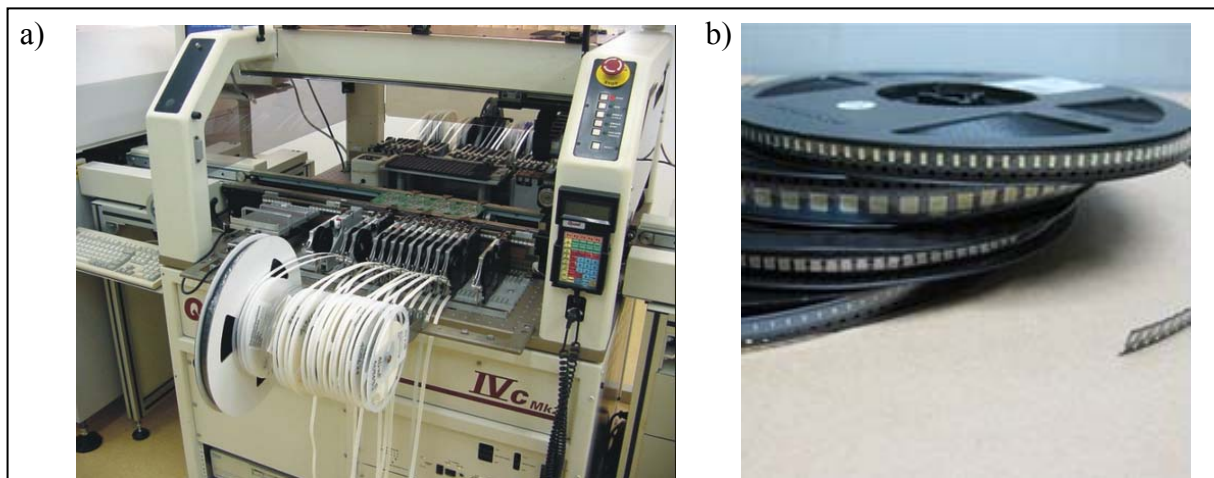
A) MÁQUINA SMD. B) ROLOS DE COMPONENTES SMD
